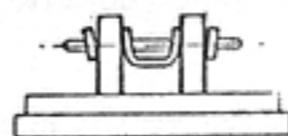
Fig. A Sistemi corretti ed errati di montaggio del gruppo interruttore della pompa
